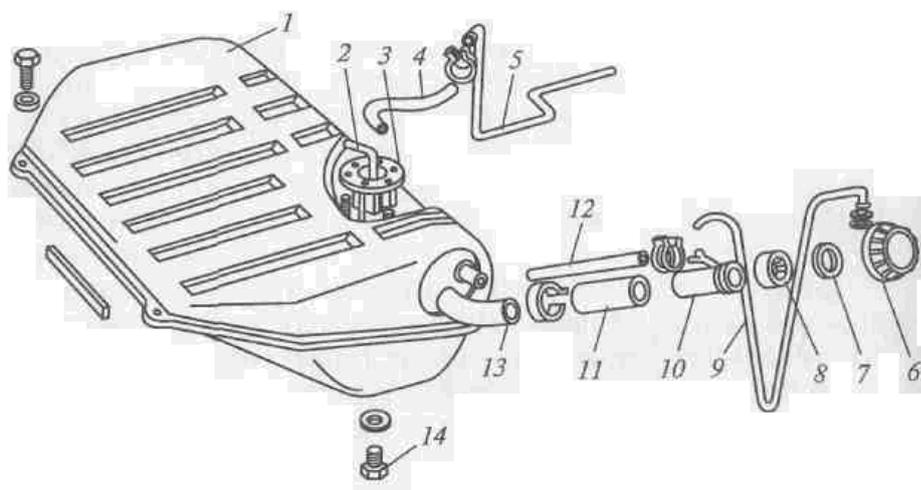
7. Топливный бак: 1 - половина бака; 2, 9, 12 -трубки; 3 - датчик; 4, 11 - шланги; 5 - топливопровод; 6, 14 - пробки; 7 - прокладка; 8 - уплотнитель; 10, 13 – трубы
